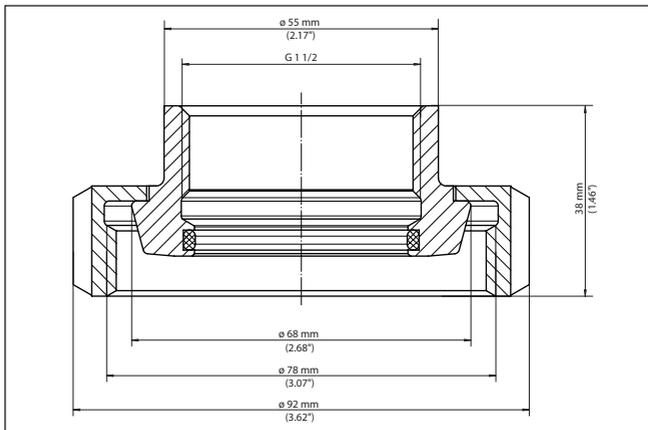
Medidas adaptador de rosca G 1½ (DIN 3852-X) sobre união rosca de tubo DN 50 (DIN 11851) PN 16
